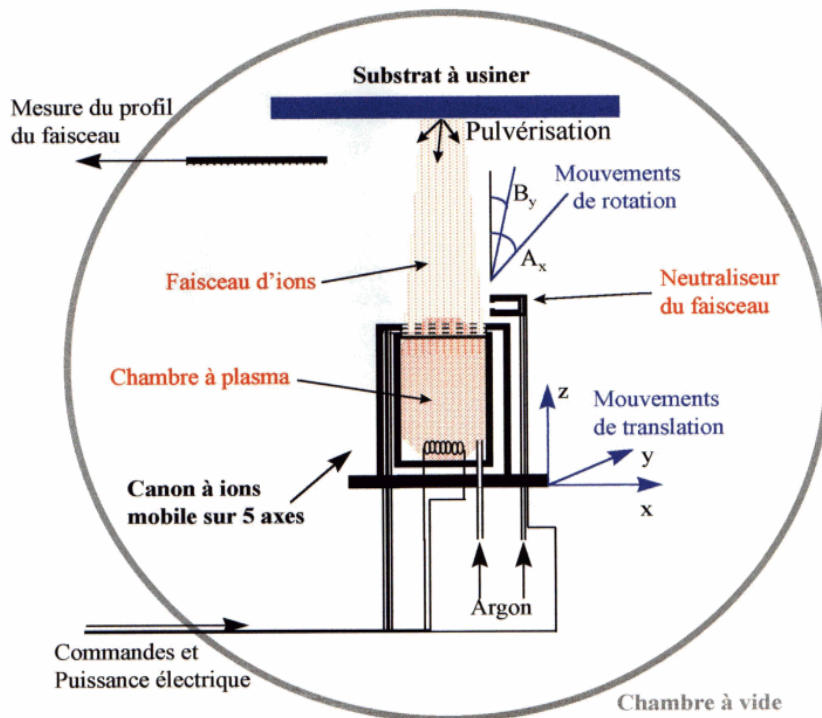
Schéma de principe du bâti d'usinage ionique de la machine Usion 1.3
